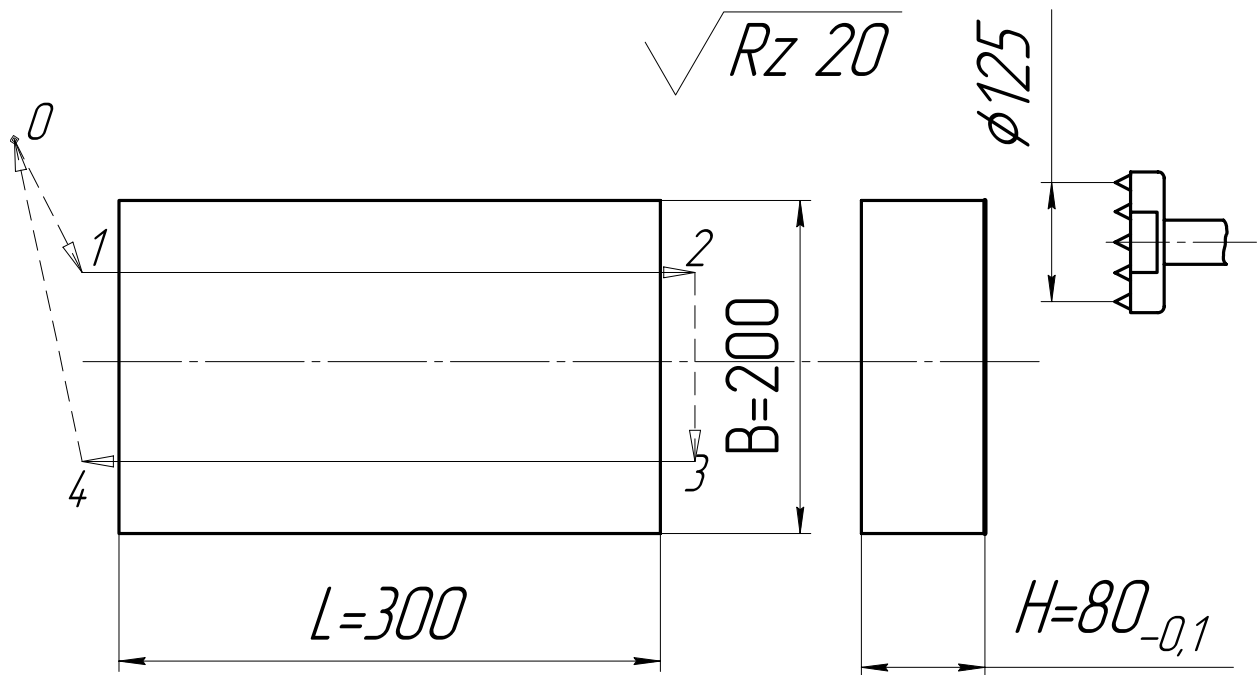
Фрезерование плоскости на станке с ЧПУ
